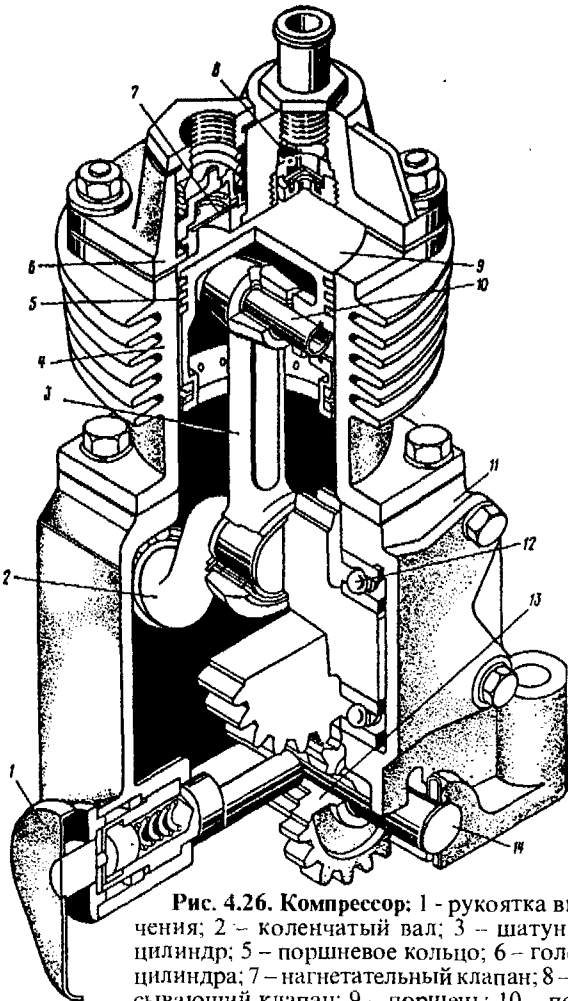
Компрессор: 1 – рукоятка включения; 2 – коленчатый вал; 3 – шатун; 4 – цилиндр; 5 – поршневое кольцо; 6 – головка цилиндра; 7 – нагнетательный клапан; 8 – всасывающий клапан; 9 – поршень; 10 – поршневой палец; 11 – картер; 12 – подшипник; 13 – промежуточная шестерня; 14 – ось
